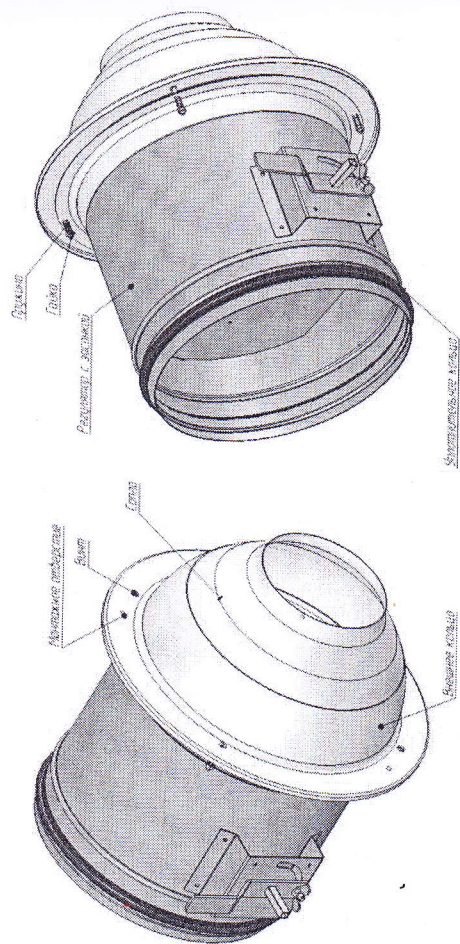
Внешний вид и конструктивная схема ЗСДР.
